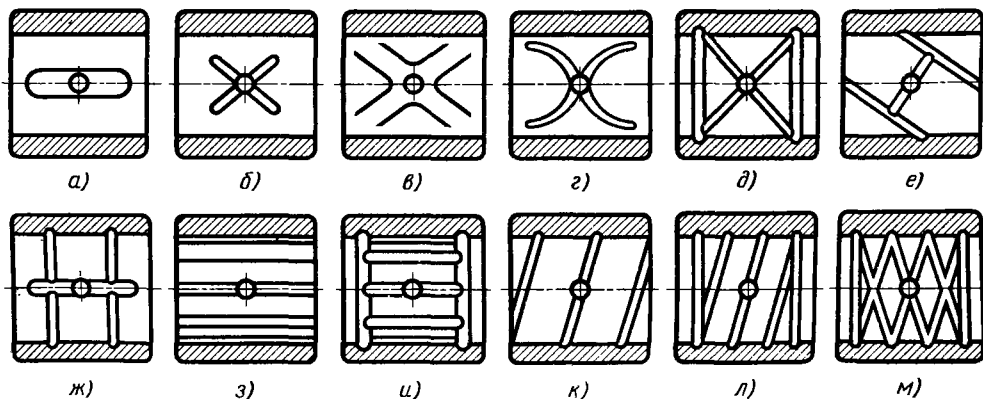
Смазочные канавки в подшипниках полужидкостной смазки
